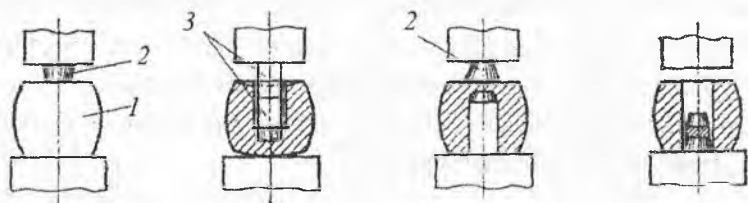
Схема прошивки: 1 - заготовка, 2 - прошивень, 3 - надставка
